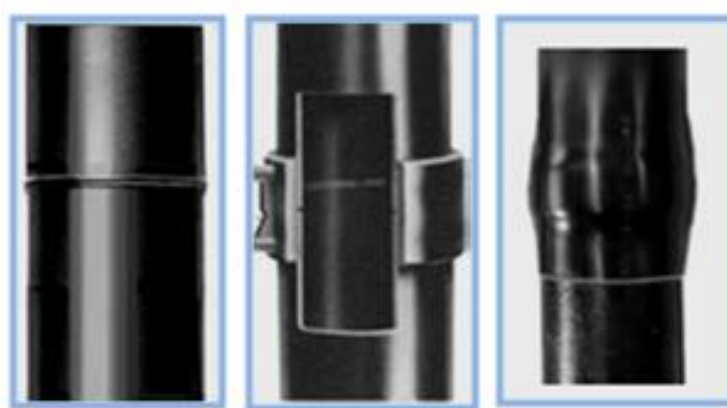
Ligação de tubos de PEAD, à esquerda através do processo de soldadura topo a topo, ao meio electrosoldadura, e à direita soldadura com manga auxiliar de polietileno [51].
